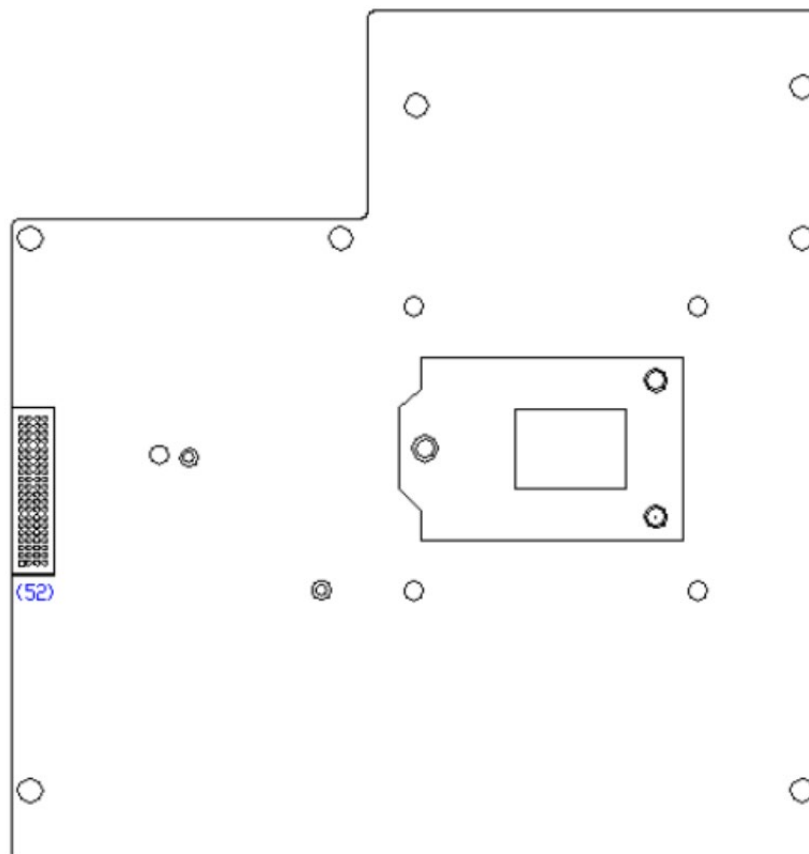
SBC-7113 - Anschlüsse und Jumper - Untersicht
